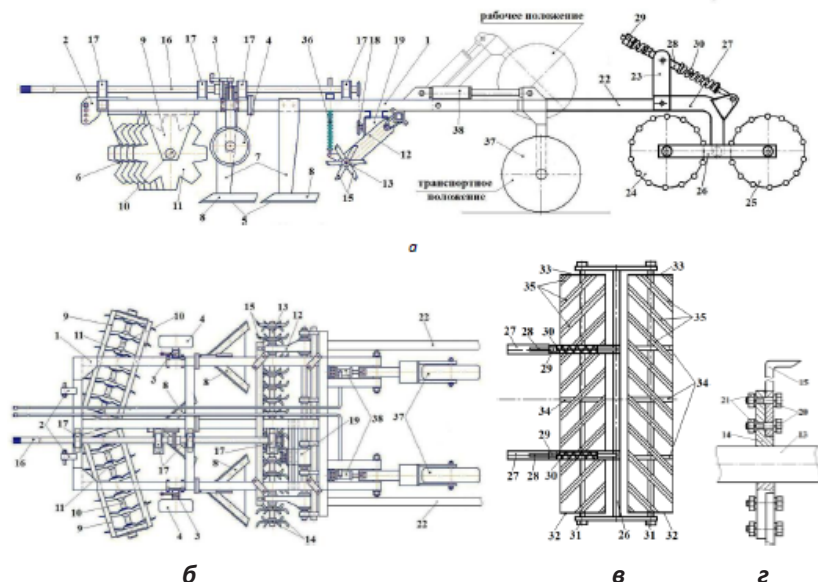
Комбинированный почвообрабатывающий агрегат (обозначения в тексте): а – вид сбоку; б – вид сверху; в – крепление Г-образных ножей; г – катковая приставка, вид сверху.
